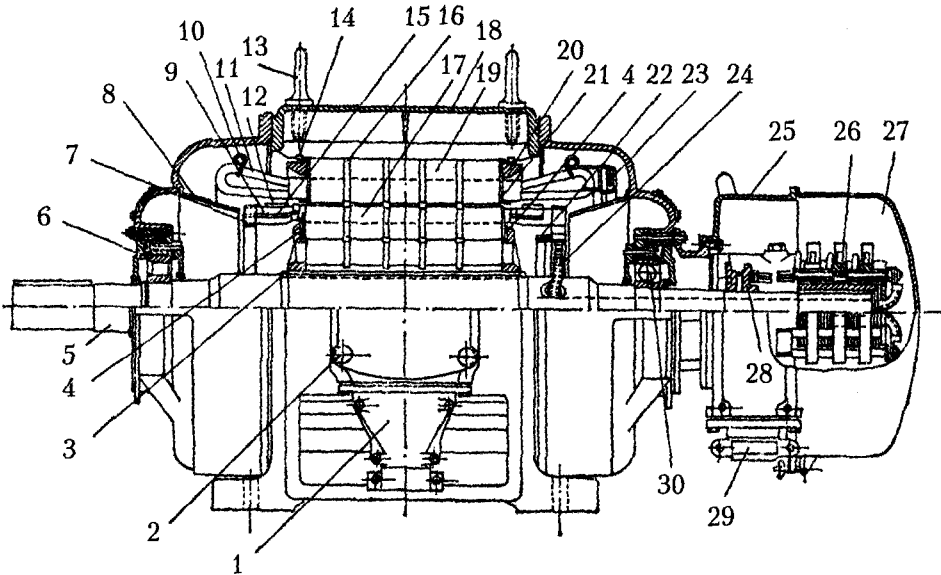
Трехфазный асинхронный двигатель с фазным ротором 180 кВт и 975 об./мин: 1 — кабельная муфта; 2 — выводная коробка концов обмотки статора; 3 — кольцевые шпонки крепления сердечника ротора; 4 — нажимные шайбы сердечника ротора; 5 — вал ротора; 6 и 30 — шариковый и роликовый подшипники; 7 — медные соединительные хомутики стержней обмотки ротора; 8 — диффузоры для направления поступающего через подшипниковые щиты охлаждающего воздуха; 9 — стержни обмотки ротора; 10 — бандажные кольца; 11 — обмотка статора; 12 — проволочные бандажи обмотки ротора; 13 — подъемные кольца; 14 — дуговые шпонки; 15 — кольцевые изоляционные прокладки; 16 — радиальные вентиляционные каналы; 17 — сердечник ротора; 18 — литой корпус статора; 19 — сердечник статора; 20 и 21 — нажимные пальцы и кольца сердечника статора; 22 — кольцо для соединения концов обмотки ротора в «звезду»; 23 — междугрупповые и междугрупповые соединения обмотки статора; 24 — выходы концов обмотки ротора к контактным кольцам; 25 и 27 — коробка и колпак контактных колец; 26 — контактные кольца; 28 — подвижная втулка с контактами для замыкания выводов и обмотки ротора накоротко; 29 — муфта для вывода концов обмотки ротора к внешней цепи
